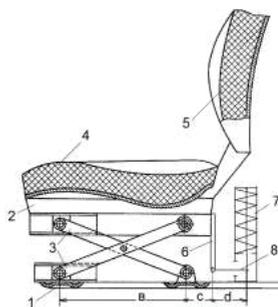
б. Общий вид подвески сиденья с направляющим механизмом типа «ножницы».
